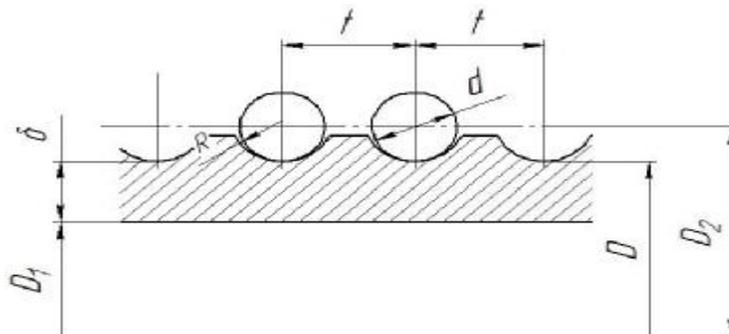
Профиль канавки для каната при однослойной навивке
